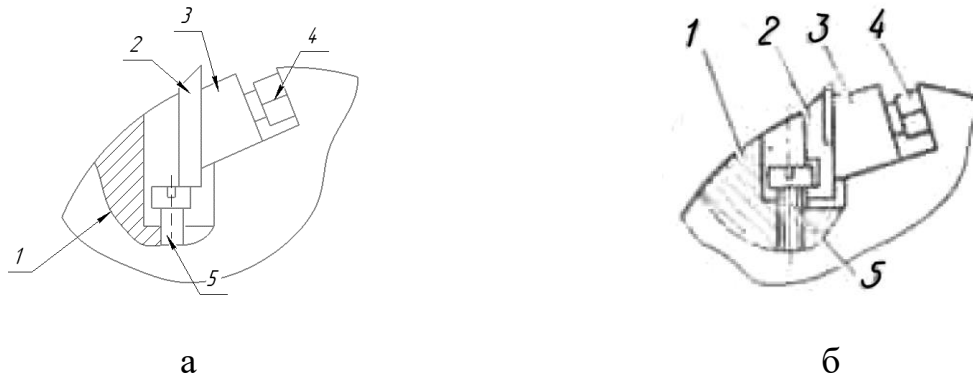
Механічне кріплення ножів в корпусі фрези
